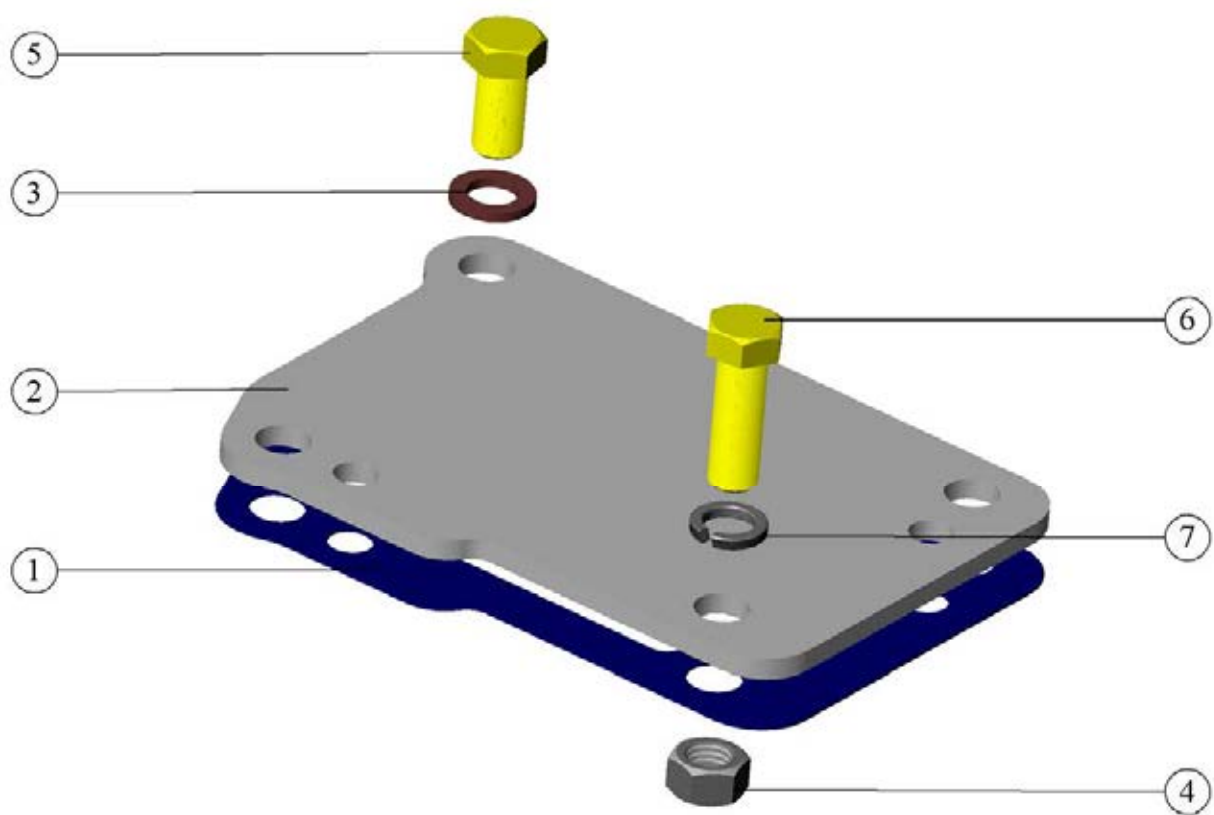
Установка заглушки (для дизелей без пневмокомпрессора)
